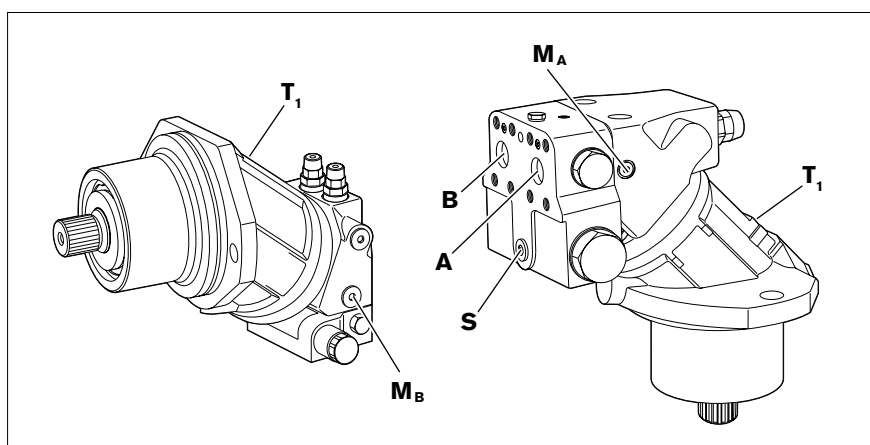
Vue d'ensemble des raccords A2FE, dimension nominale 28 à 180, plaque de raccordement 181 avec valve de freinage rapportée, raccords de service en bas
